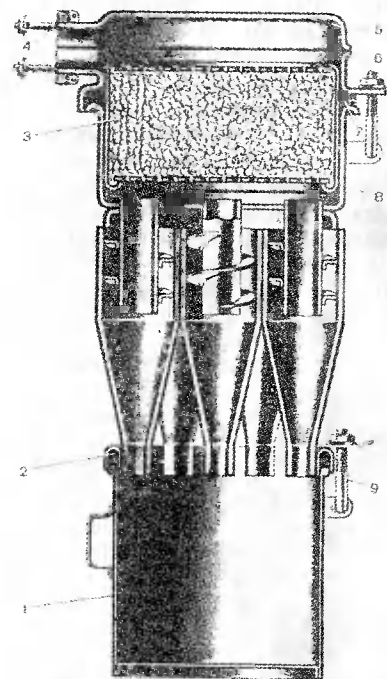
Воздухораспределитель: 1 — бункер; 2, 7 — войлочные прокладки; 3 — кассета; 4, 6, 9 — стяжные болты; 5 — головка; 8 — корпус
